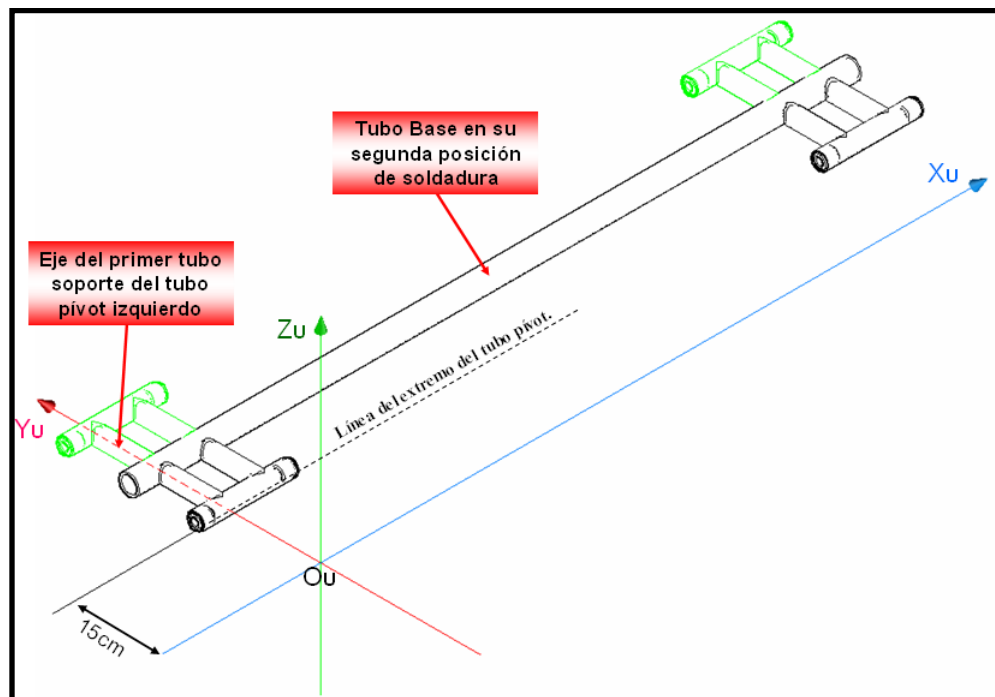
Enumeración de la secuencia de soldadura del Tubo Base
